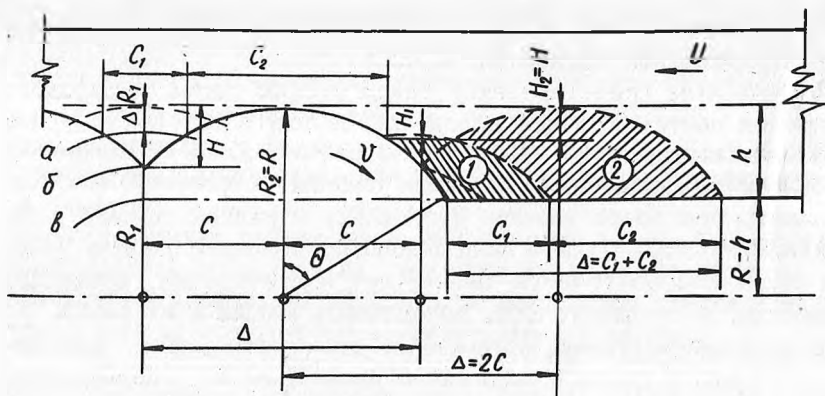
Схема образования поверхностей резания для двух-резцовой фрезы.
